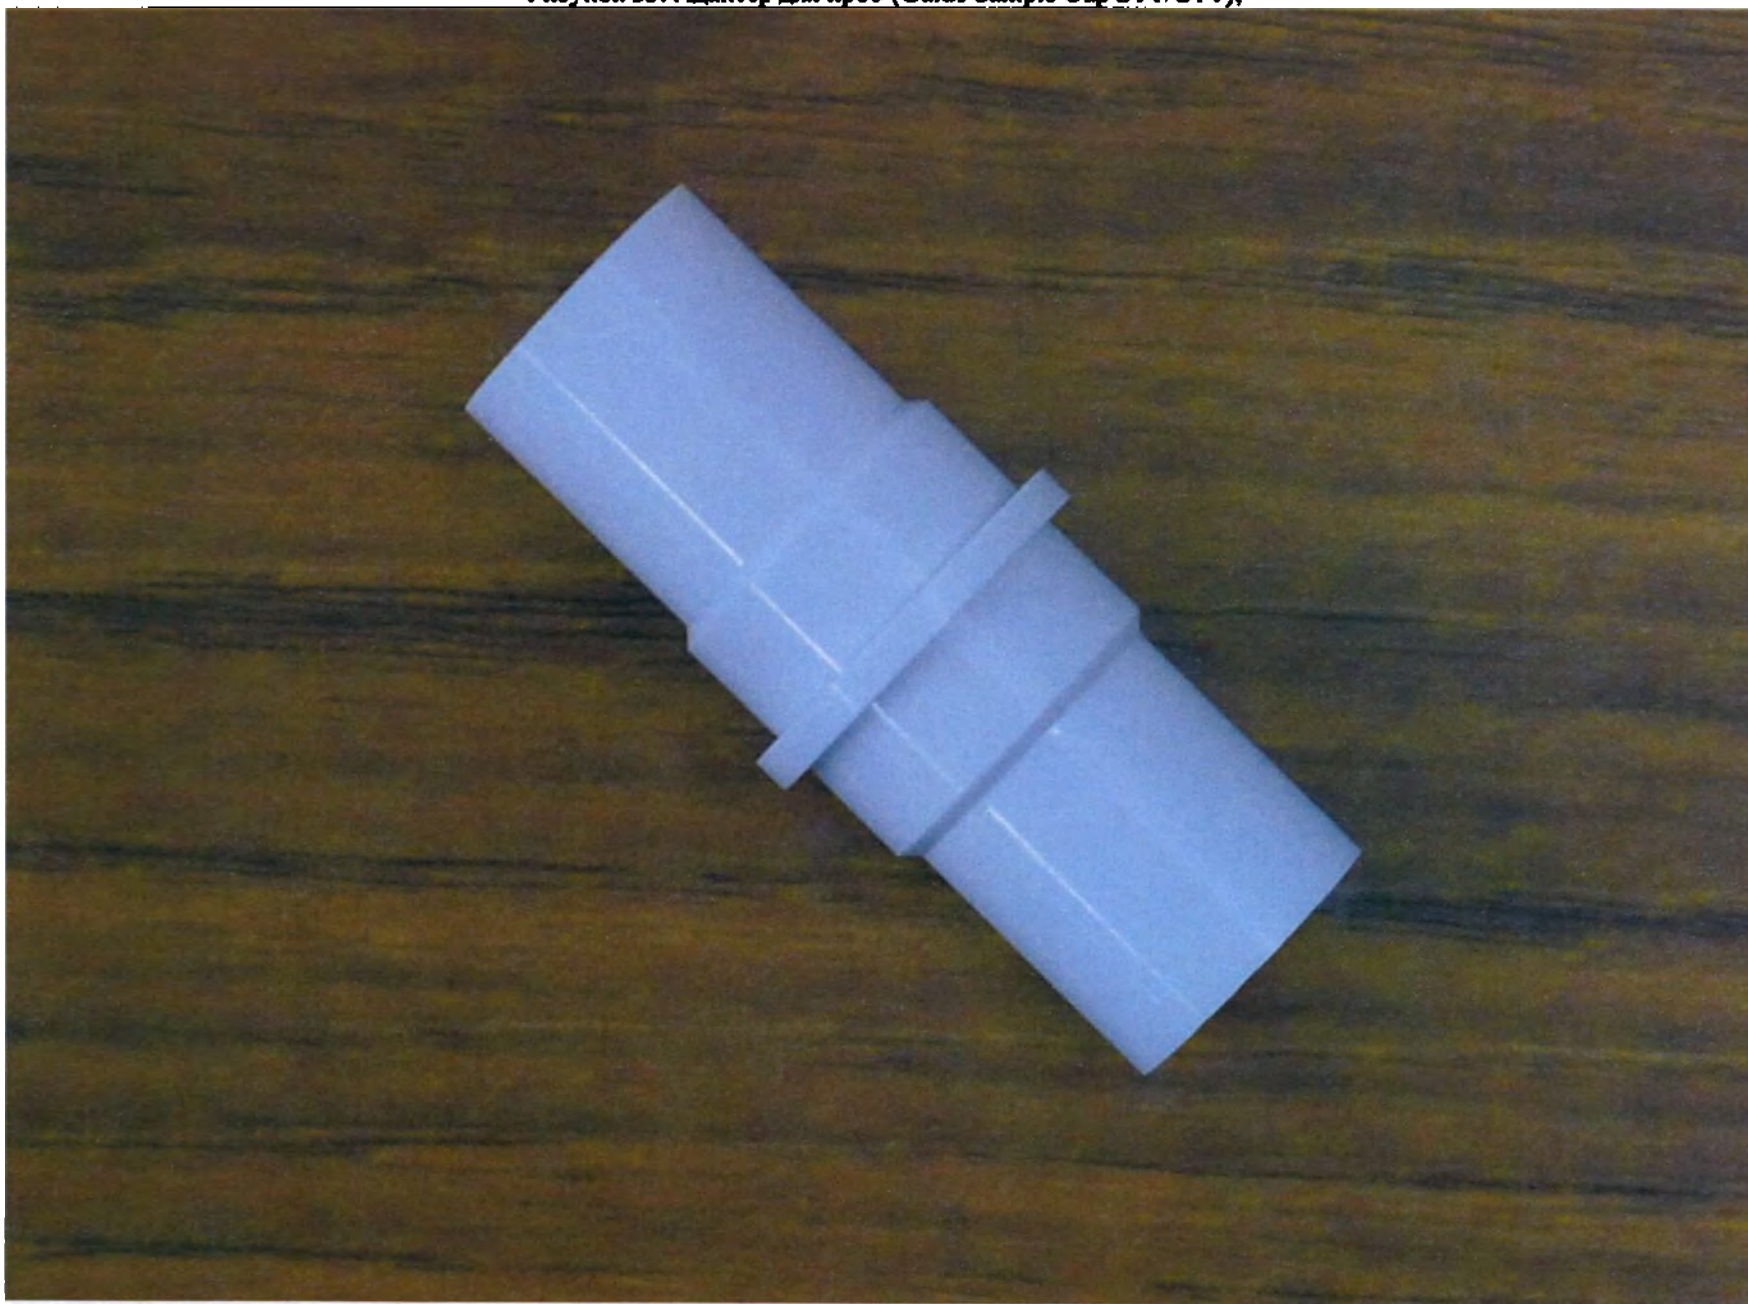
Приспособление для LWP (сокет) (Jig LWP (Socket));
